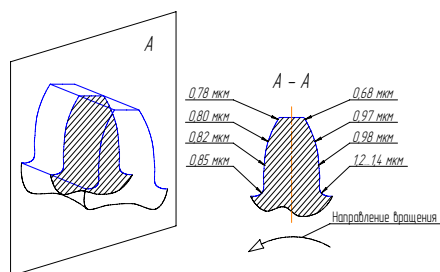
Шероховатость рабочей поверхности зуба ( $m = 2,5$  мм) после MAO
